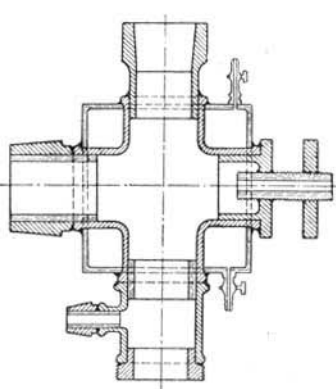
Zusammengeschweißte, mit Kühlmantel.
